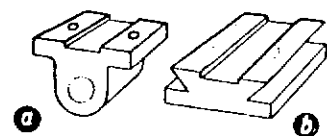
Ejemplos del esmerilado plano. a) Esmmerilado basto de una superficie de apoyo; b) afinado por esmerilado de una superficie de desbastamiento.
